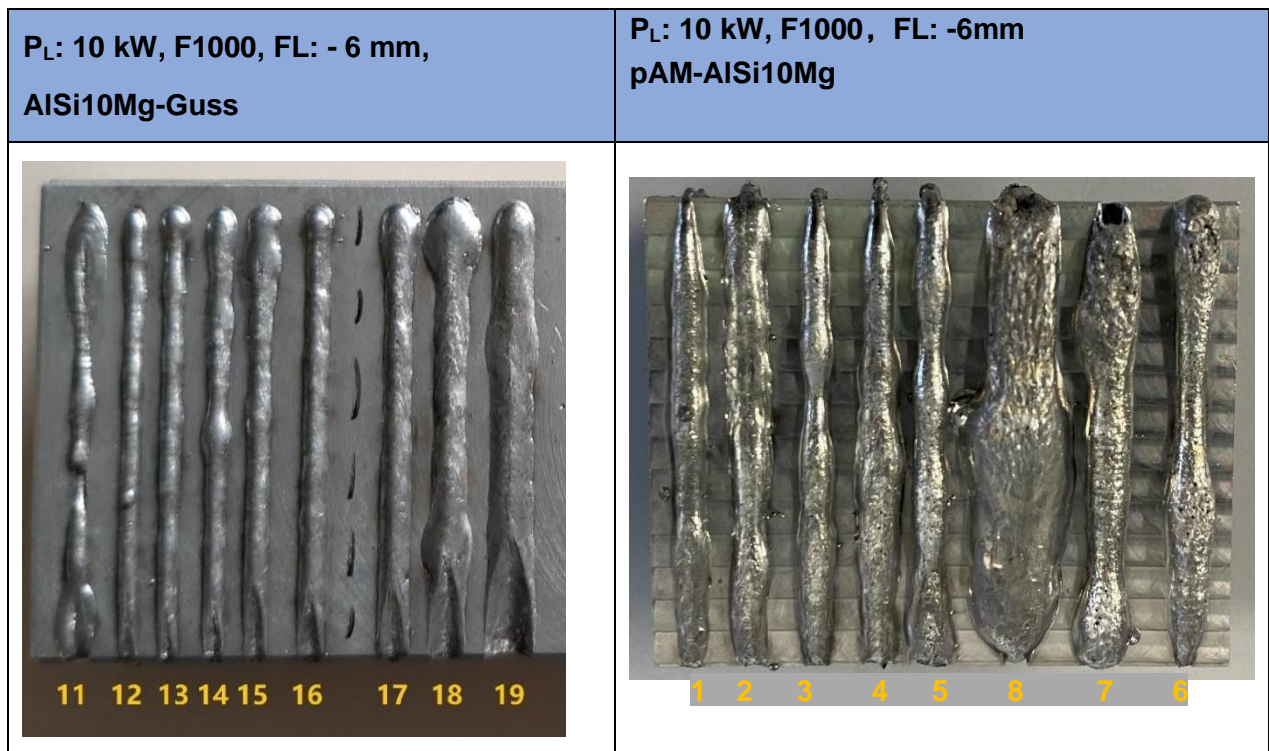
Schweißnahtoberraupen bei unterschiedlichem Material für FL: - 6 mm
